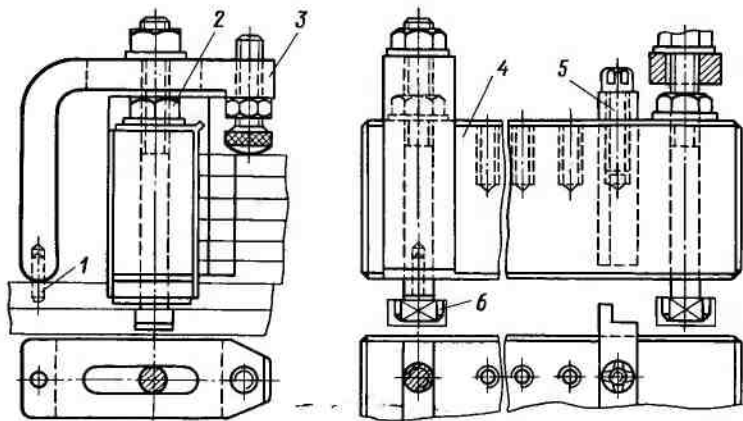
Приспособление для фрезерования торцовых поверхностей
